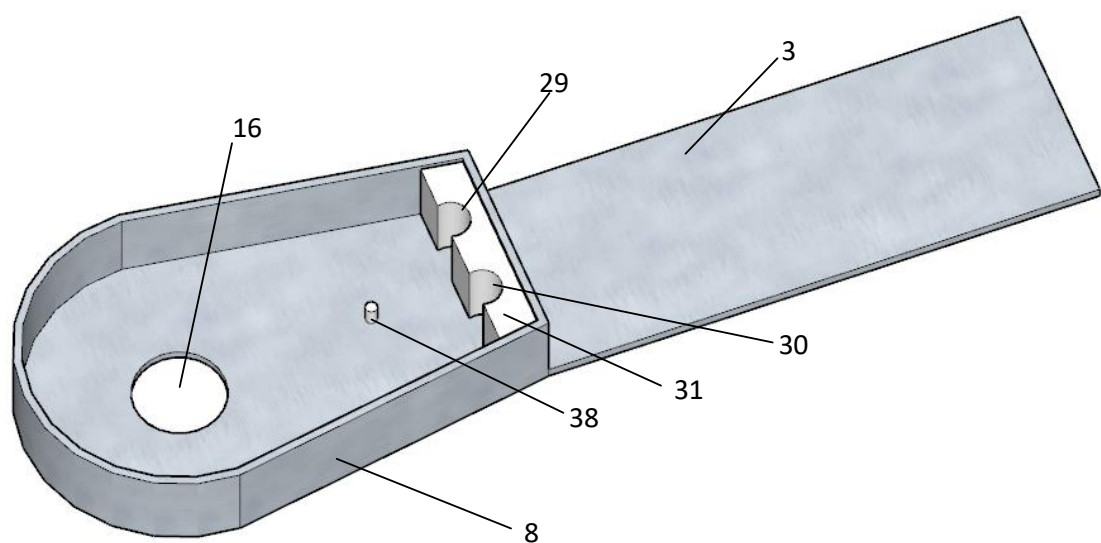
Шина плеча з коробчастим корпусом механізму редресації
